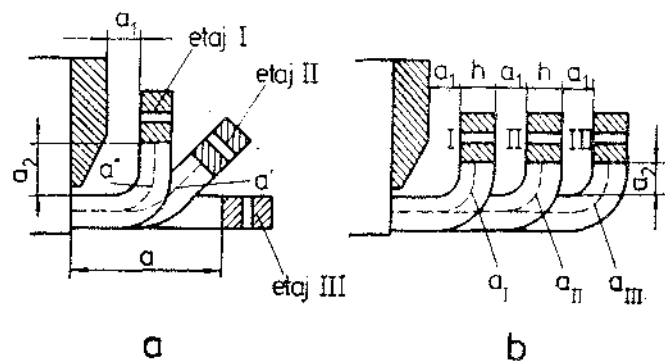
Forma și dimensiunile capetelor de bobine, în trei etaje și cu $q = 4$:
